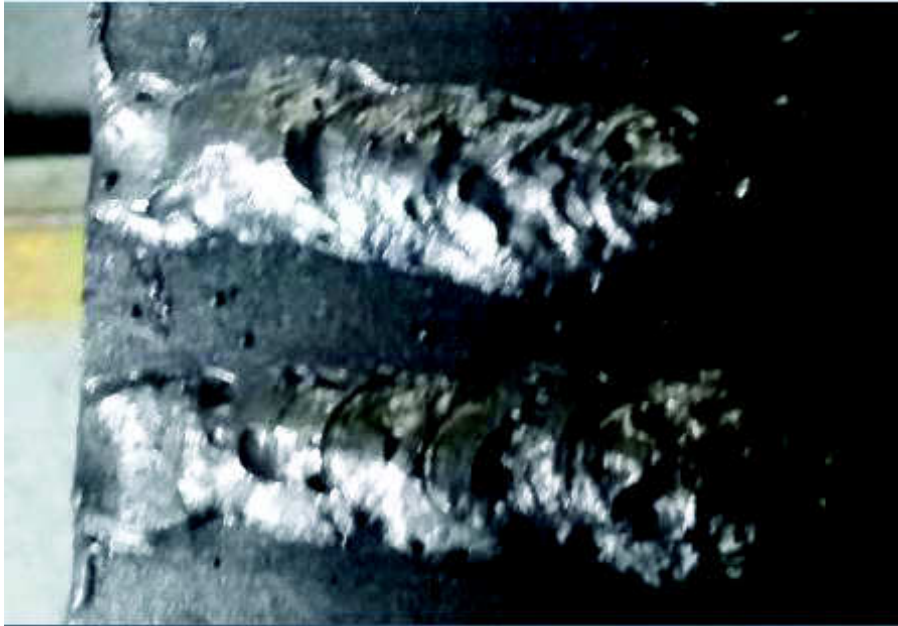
Cordões de Solda obtidos em Soldagem com Eletrodo Revestido com Resina Epóxi RenLam M (com 6% de Feldspato de potássio – fotografia sem ampliação).
